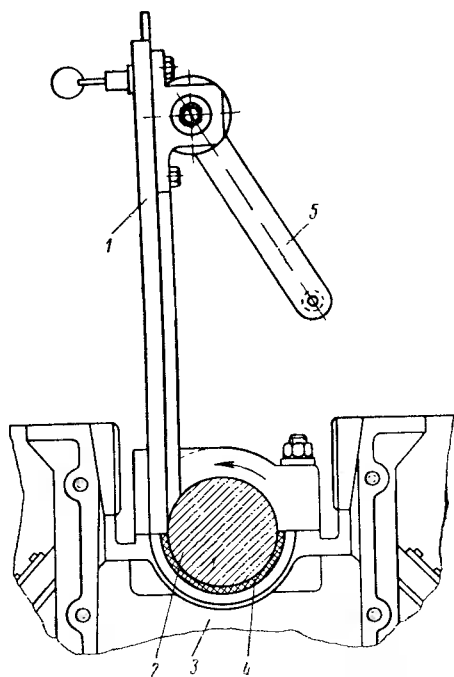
Приспособление для запрессовки сальника в блок цилиндров:
